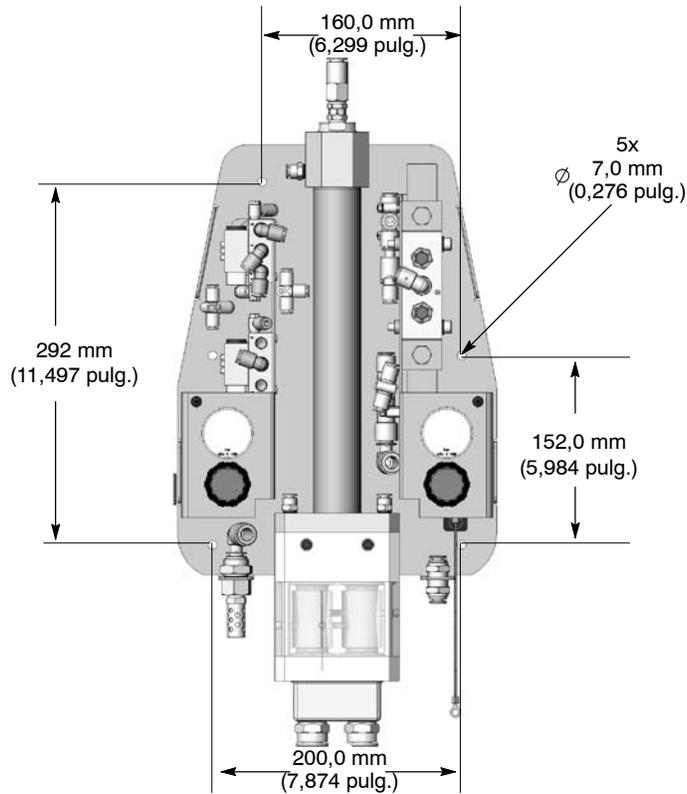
Dimensiones de la bomba HDLV de alta capacidad Prodigy
